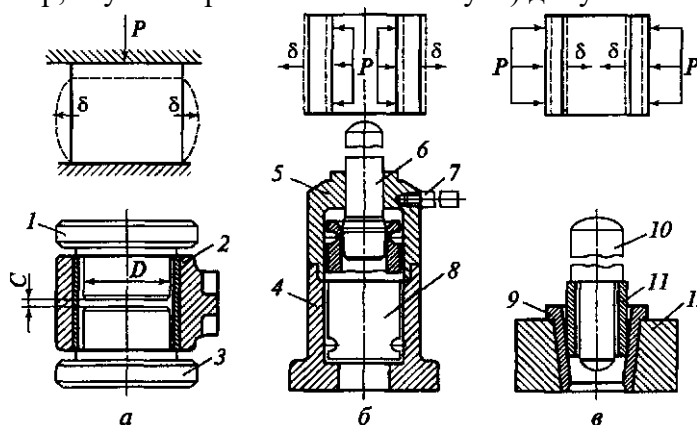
Схемы восстановления деталей способами давления: а - осадка; б - раздача; в - обжатие; 1, 3 - оправки; 2, 11 - втулки; 4, 5 - нижняя и верхняя части кондуктора; 6 - прошивка; 7 - ручка; 8 - поршневой палец; 9 - кондуктор; 10 - толкатель; 12 - матрица; P - внешняя сила; δ - направление деформации; C - зазор между оправками; D - диаметр оправки
